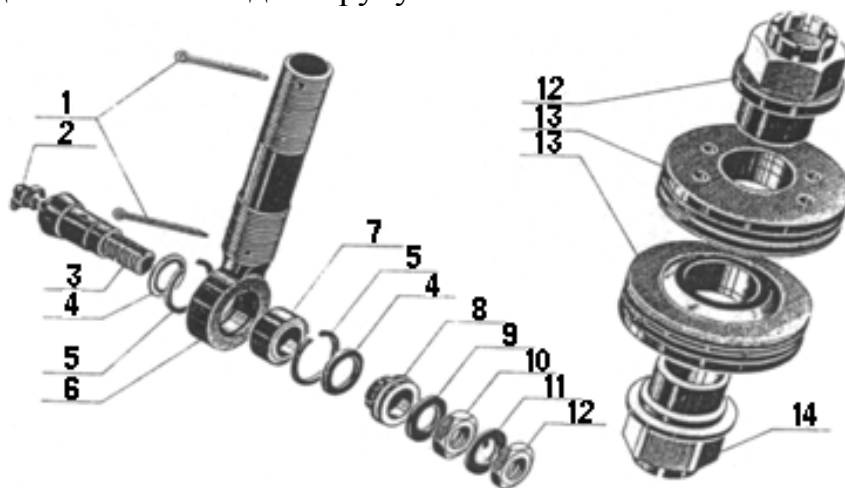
Підвіска тягового редуктора (верхня частина):
